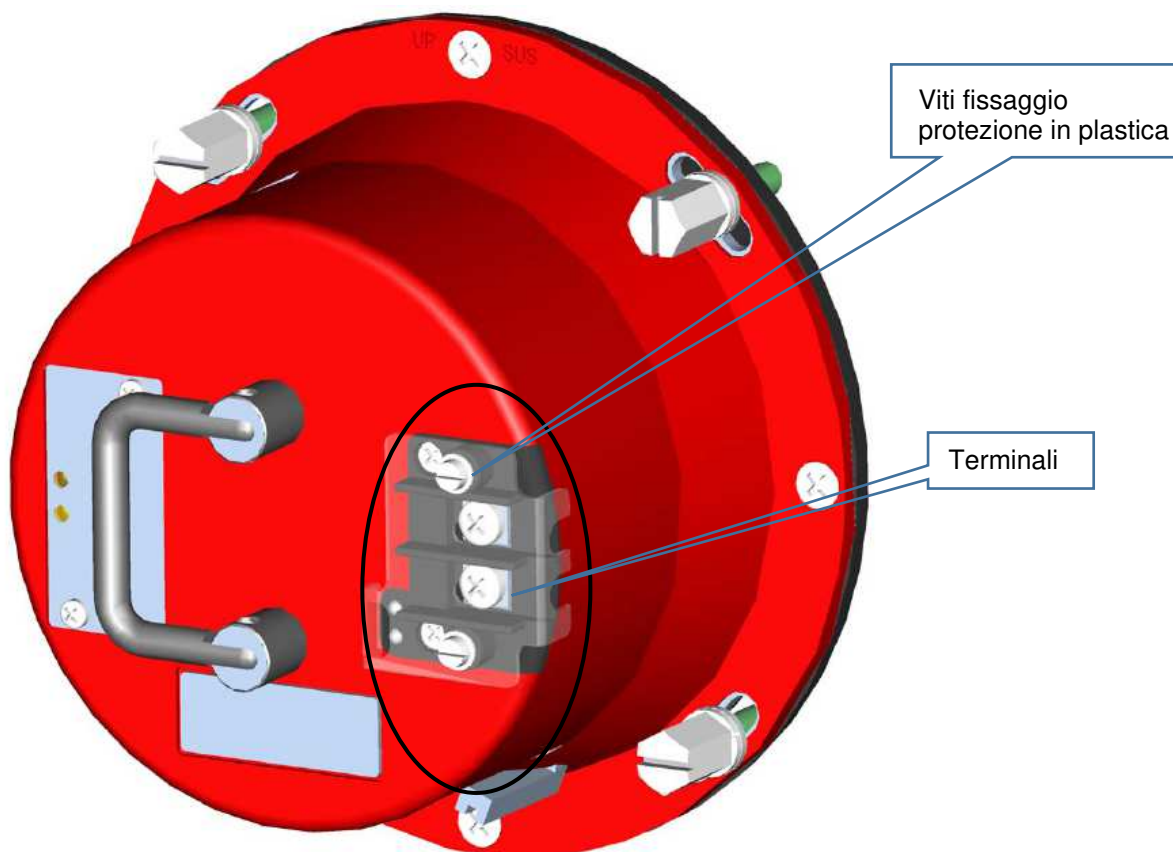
Protezione plastica della morsettiera da rimuovere temporaneamente per il collegamento dei cavi di alimentazione alla SL-LED
